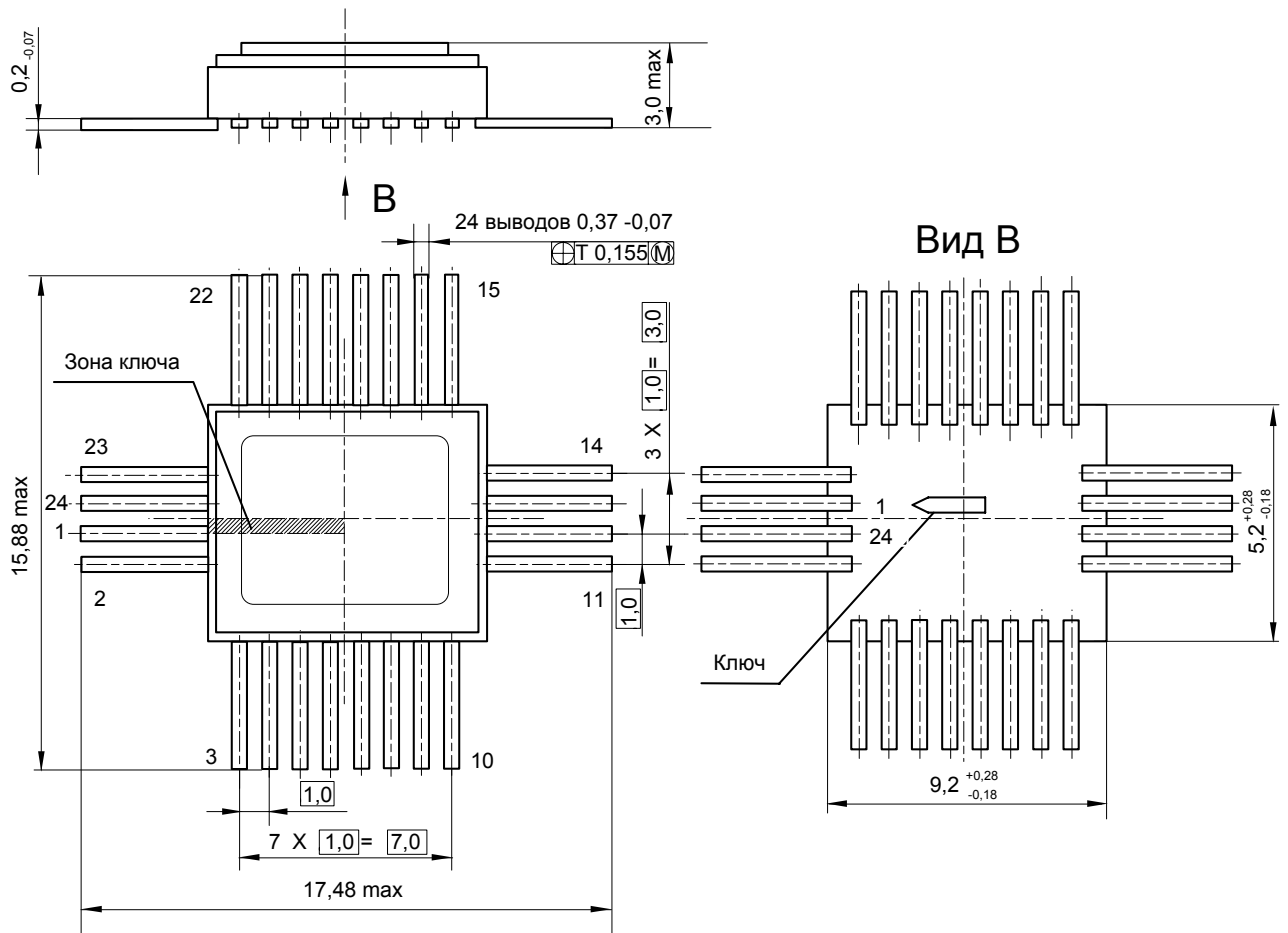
Габаритный чертеж микросхемы в корпусе H06.24-2B
